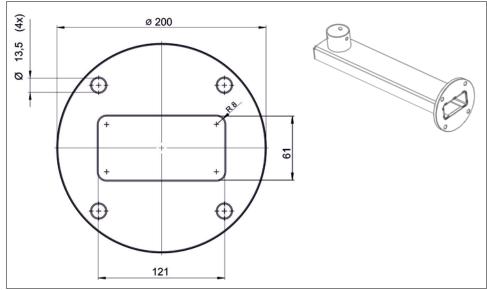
Gabarit de perçage - Support pour fixation murale
